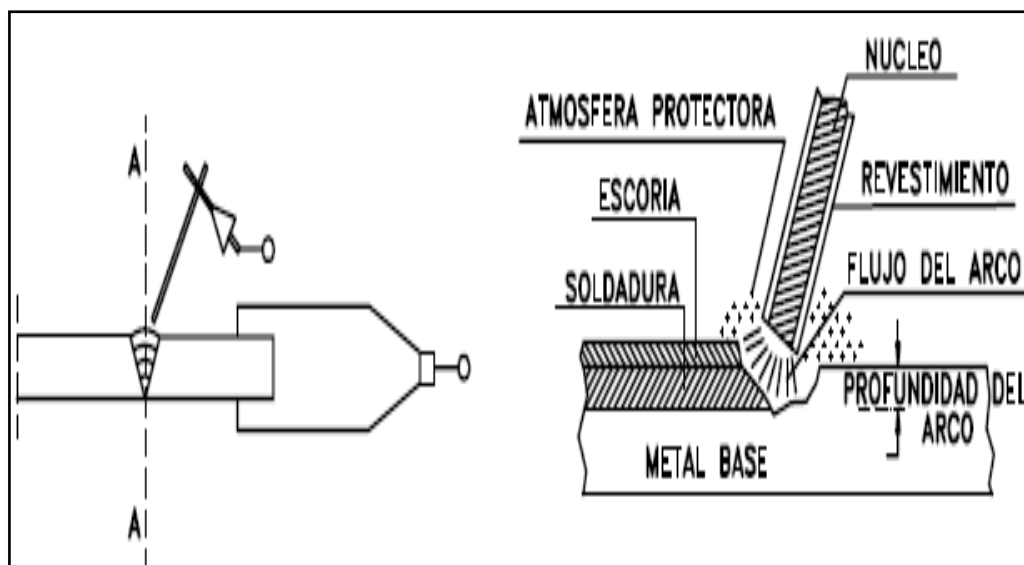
Soldadura con electrodo metálico revestido
